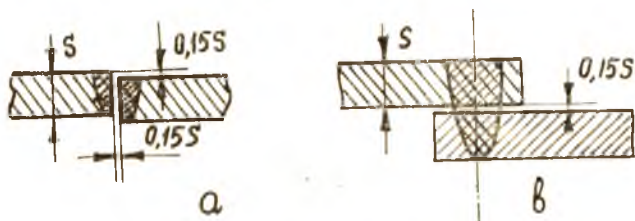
Схемы расположения заготовок при лазерной сварке стык (а) и внахлест (б)
